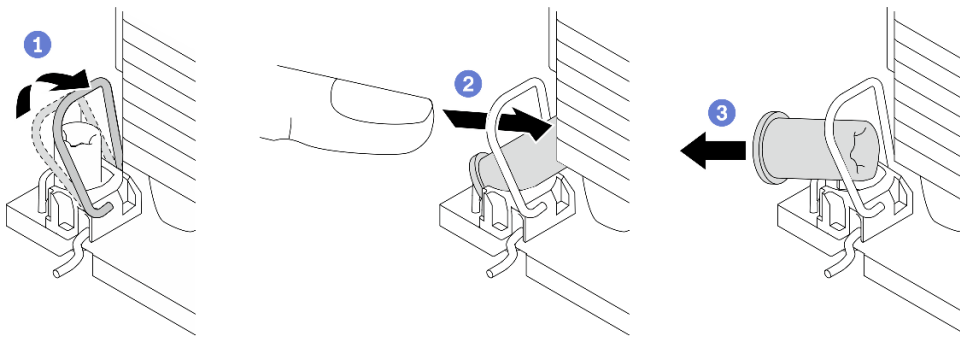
Entfernen einer T30-Torx-Mutter vom Kühlkörper
